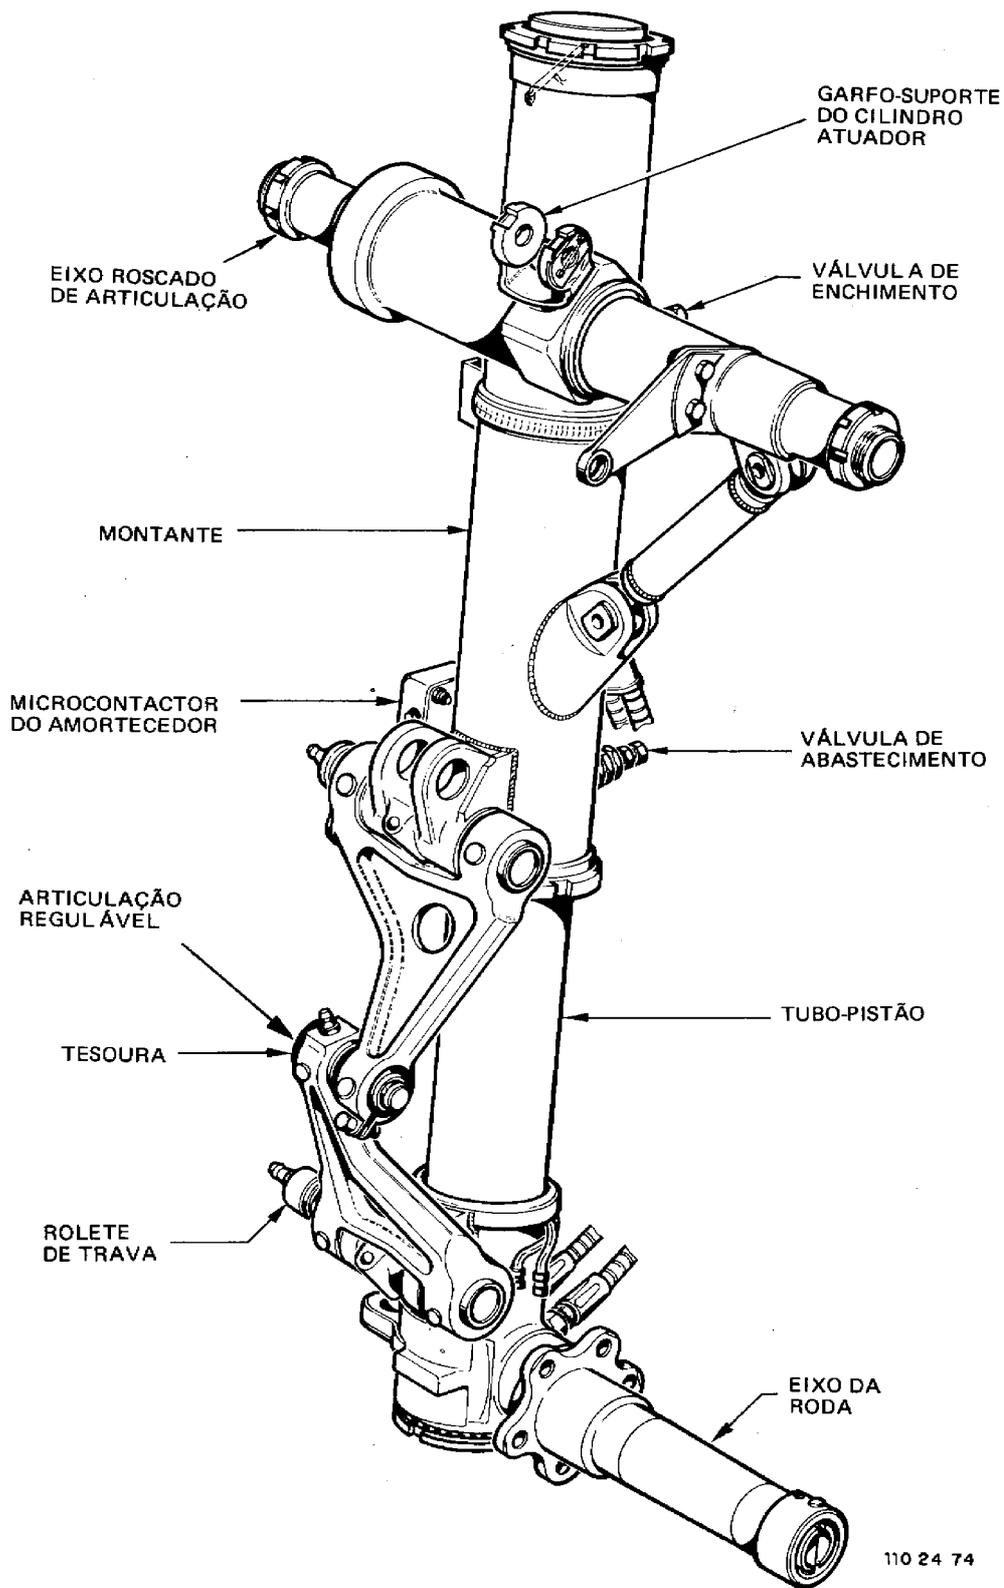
Montante e Amortecedor do Trem de Pouso Principal
